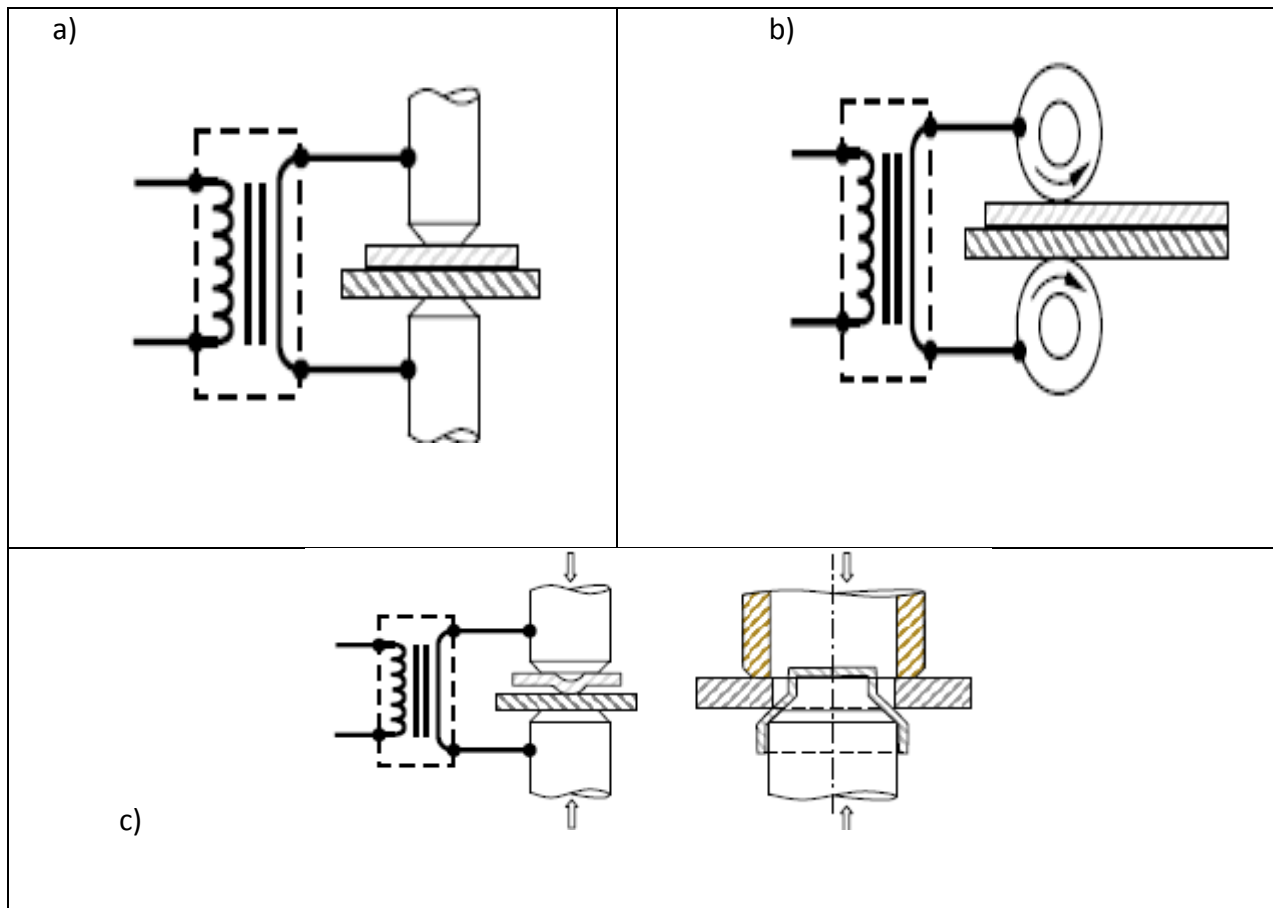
Procédés de soudage par résistance électrique, a) soudage par points, b) soudage à la molette, c) Le soudage par bossages [3].
